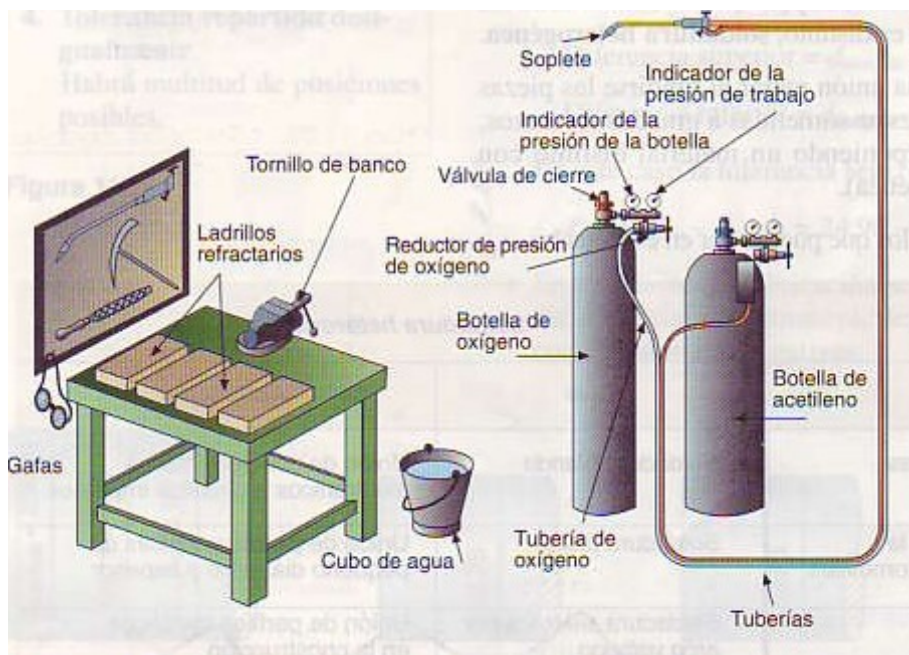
Elementos de que consta un equipo de soldadura oxiacetilénica
